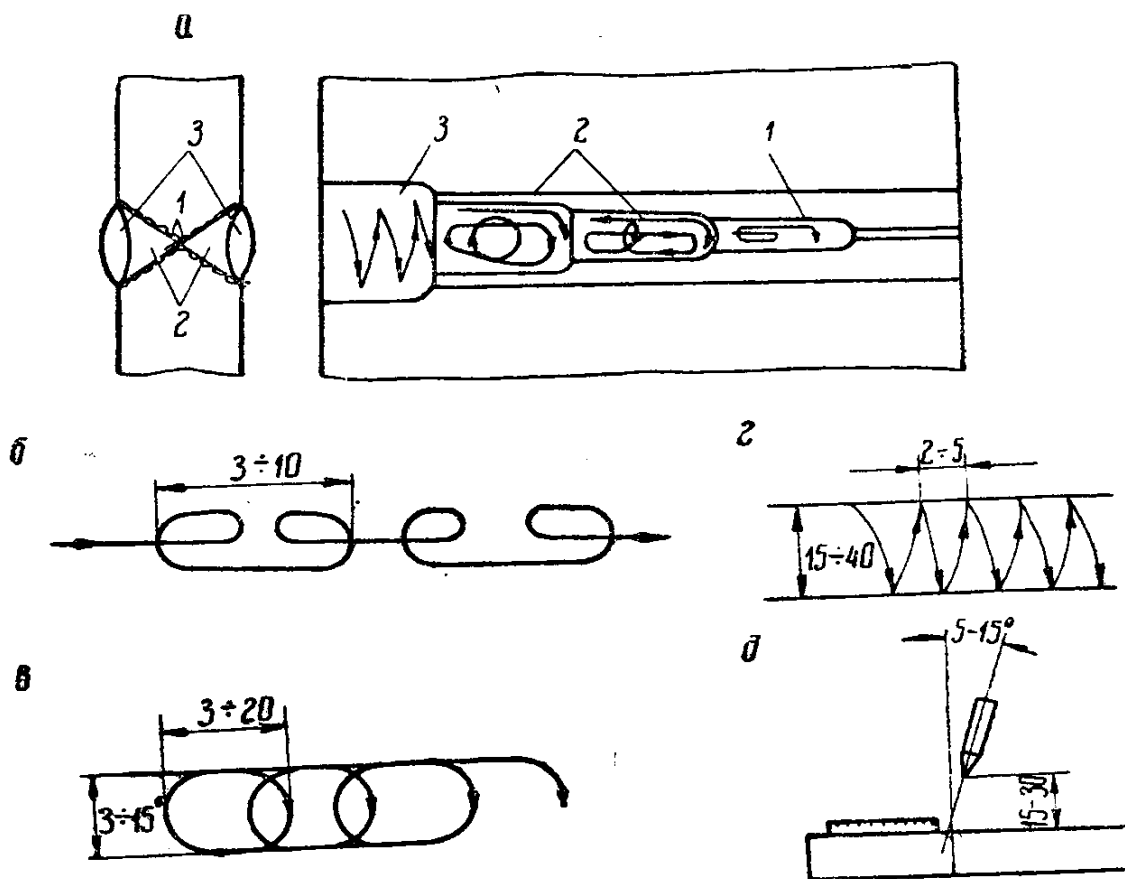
Положение и схема перемещения горелки (электрода) при полуавтоматической сварке стыковых швов в углекислом газе: *а* — порядок наложения стыковых швов: *1* — первый и подварочный слой; *2* — средние слои; *3* — верхние слои; *б* — возвратно-поступательное перемещение горелки вдоль оси шва; *в* — перемещение горелки (электрода) по вытянутой спирали; *г* — перемещение горелки «змейкой»; *д* — положение горелки при сварке.
